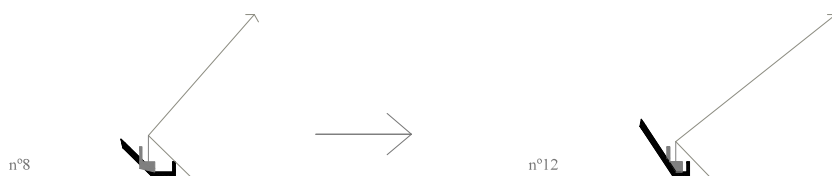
Tipo 3. Elaboración propia.
